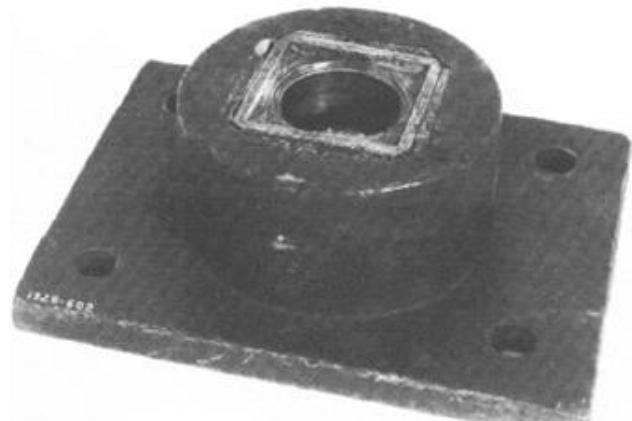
Cojinete de inicios del siglo XIX [13].
